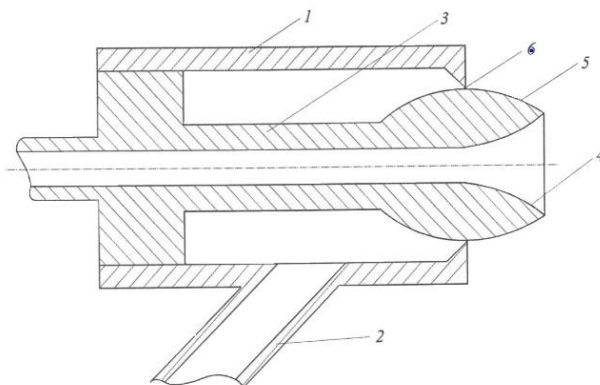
Продольный разрез пневматической форсунки для распыла ВУТ: 1 – корпус с патрубком; 2 – патрубок для подачи сжатого воздуха; 3 – труба для подачи ВУТ; 4 – диффузорное сопло; 5 – кольцевая насадка; 6 – кольцевое газовое сопло
